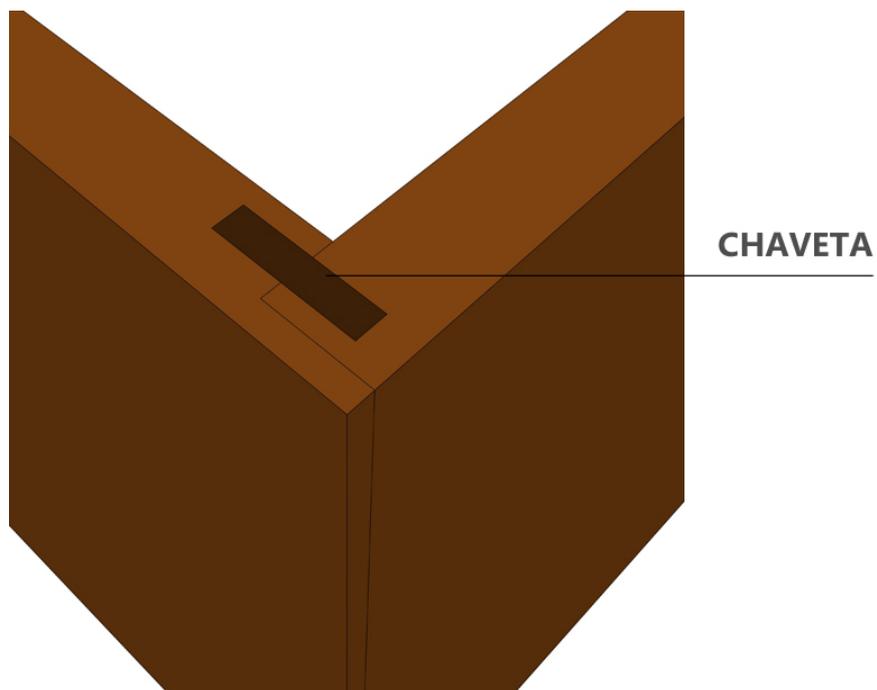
Esquema de quina frontal de gaveta com união em chaveta.
